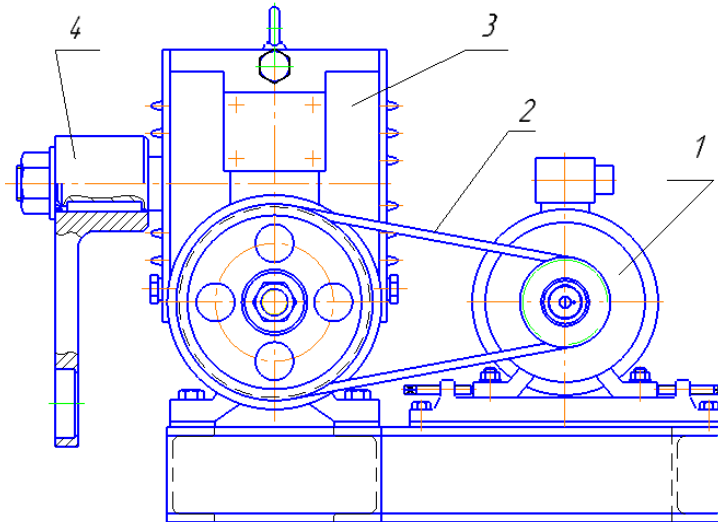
Привод укладальника : 1. двигун ; 2.- клино пасова відкрита передача; 3.-черв'ячний редуктор; 4.- приводний кривошип.
